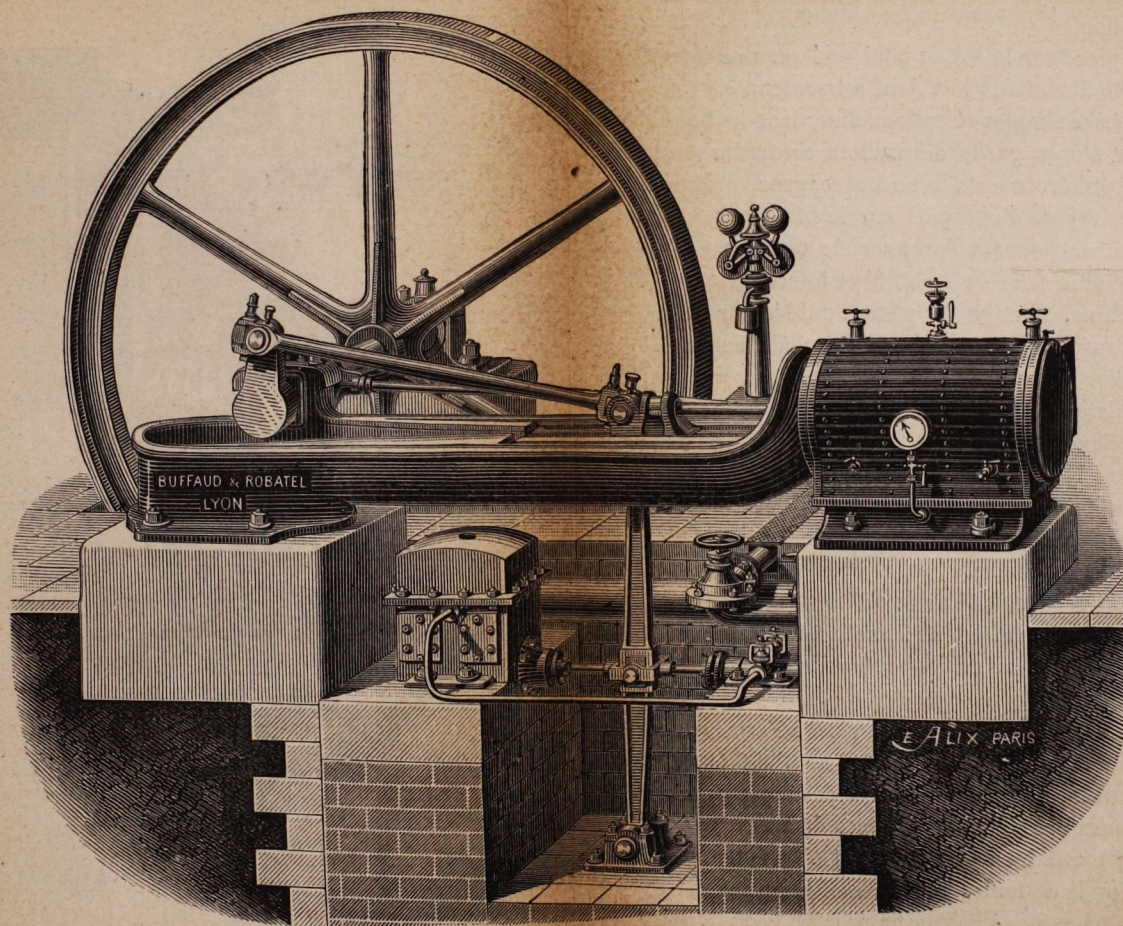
Machine horizontale Buffaud et Robatel (voy. page 182).
